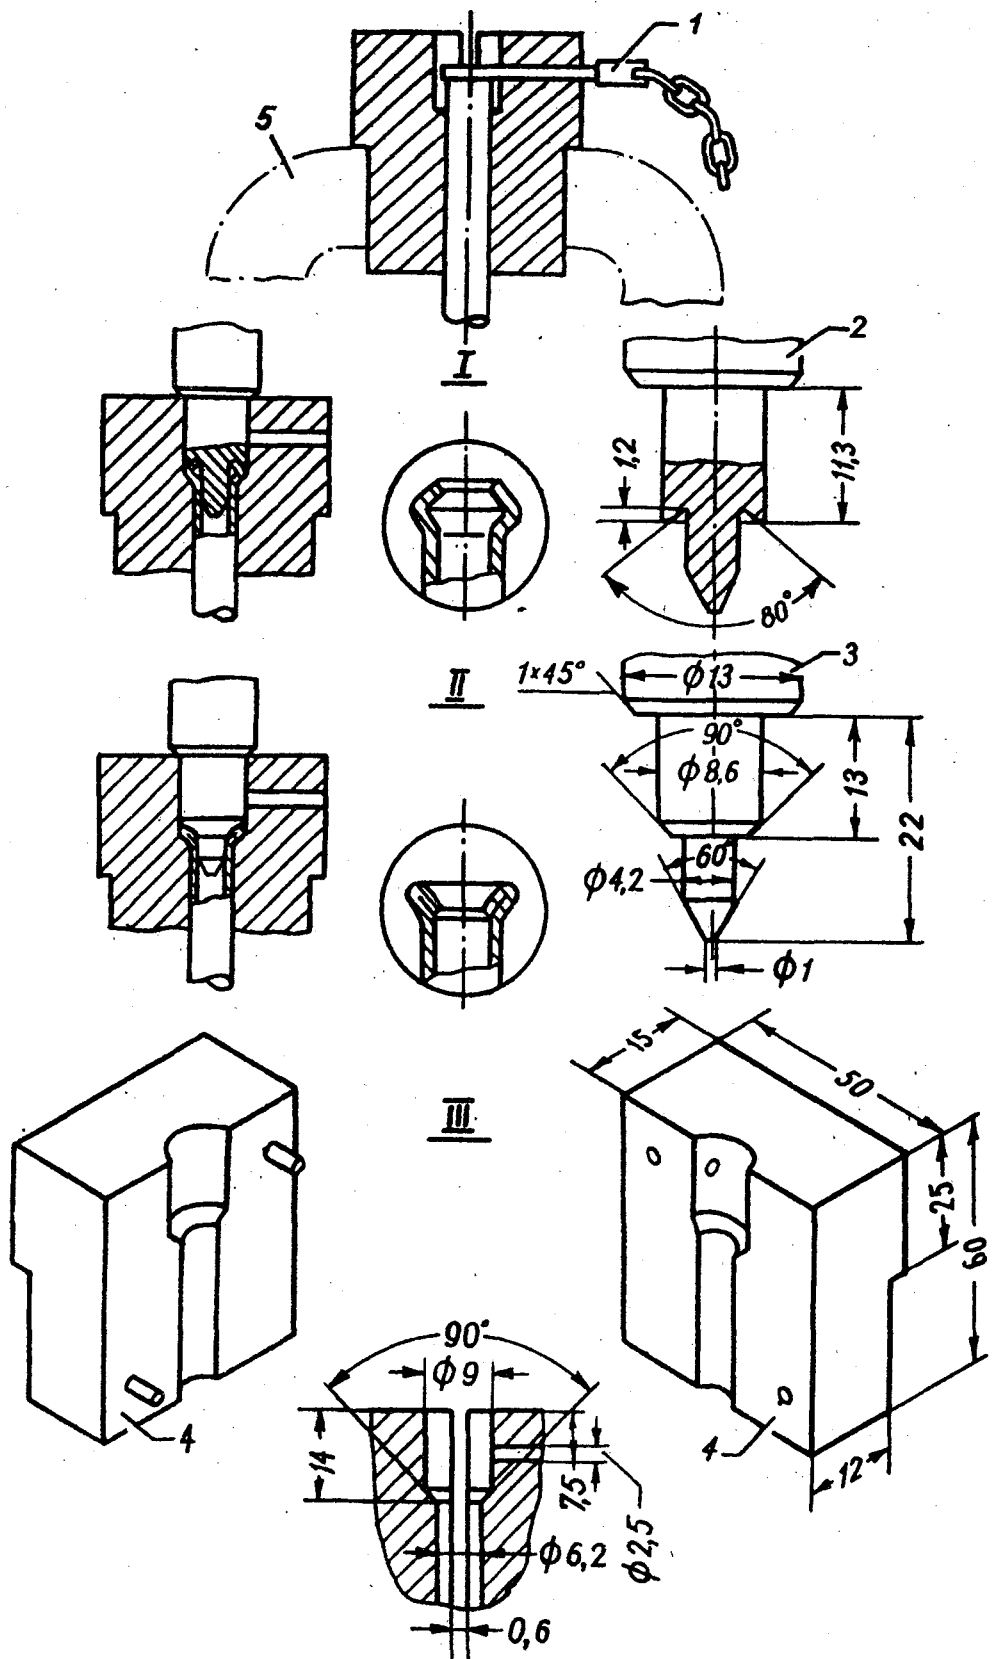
Двойная развальцовка трубок гидропривода тормозов:
